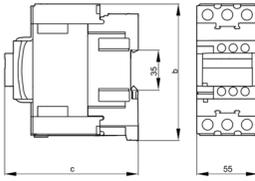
Габаритные размеры контакторов ПК-340XX - ПК-350XX
